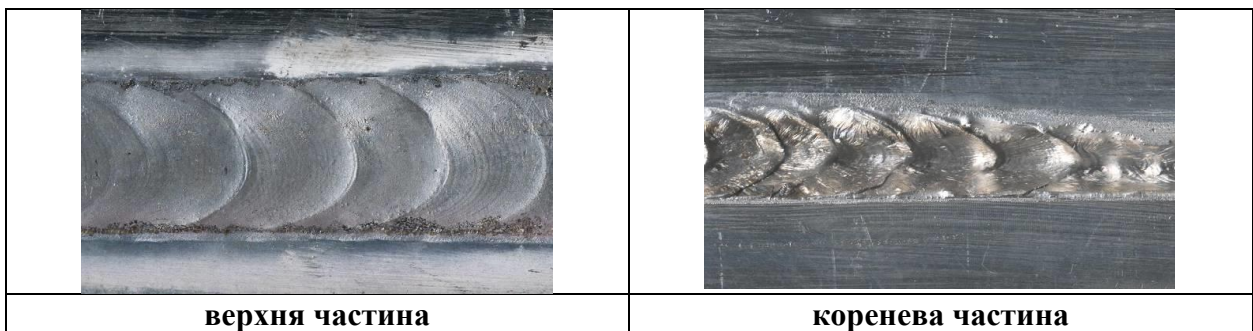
Верхня та коренева частини зварного з'єднання листів товщиною 6 мм сплаву АМг6, сформованого при плазмо-дуговому зварюванні у нижньому положенні з використанням сталеві підкладки з канавкою розмірами 4x1 мм.
